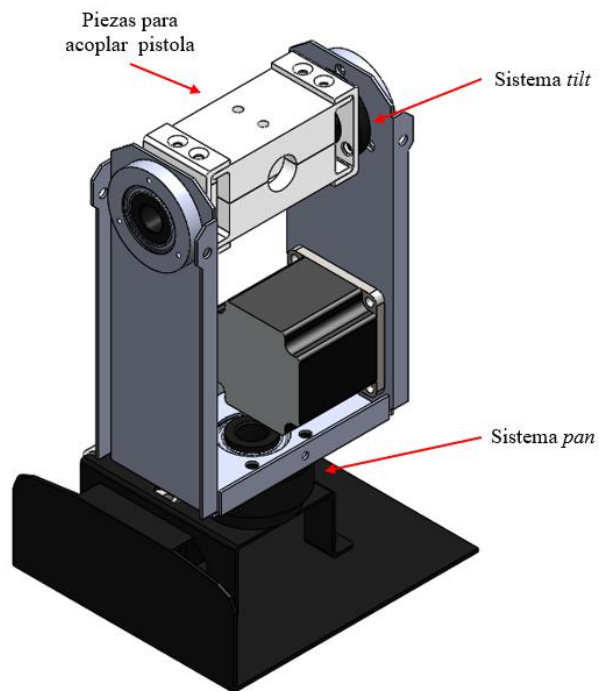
Vista isométrica del diseño CAD del sistema *pan-tilt*.
